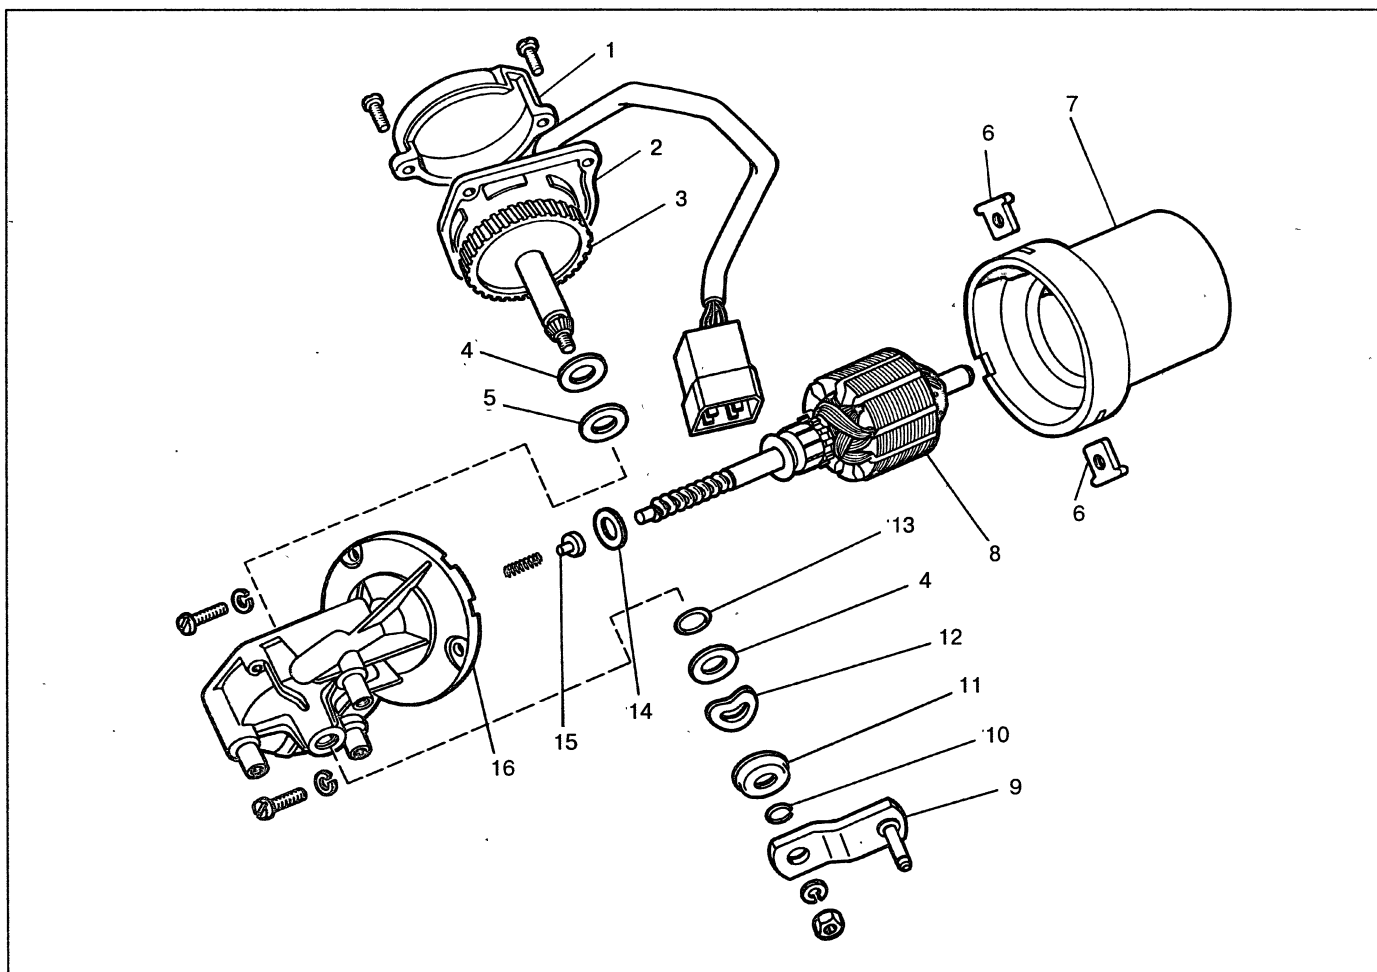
Детали моторедуктора очистителя ветрового стекла: 1 – крышка; 2 – панель; 3 – шестерня редуктора; 4 – стальная шайба; 5 – текстолитовая шайба; 6 – сухарь; 7 – корпус; 8 – якорь; 9 – кривошип; 10 – стопорное кольцо; 11 – защитный колпачок; 12 – пружинная шайба; 13 – уплотнительное кольцо; 14 – регулировочная шайба; 15 – подпятник; 16 – крышка электродвигателя
